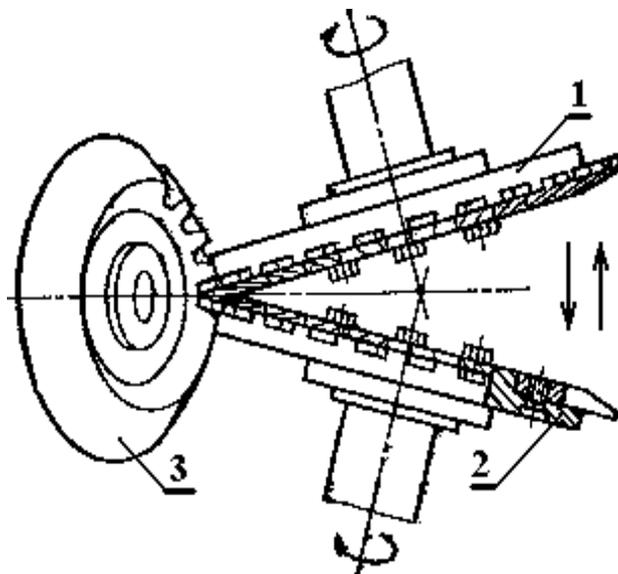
Схема 2-х дискового зубофрезерования.
